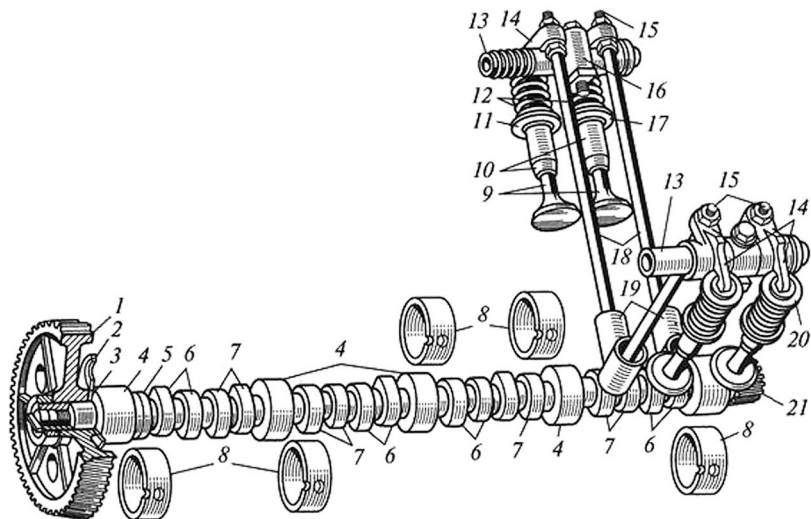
Газораспределительный механизм V-образного двигателя: 1 – зубчатое колесо; 2 – упорный фланец; 3 – распорное кольцо; 4 – передняя опорная шейка; 5 – эксцентрик; 6, 7 – соответственно впускные и выпускные кулачки; 8 – опорные втулки; 9 – клапаны; 10 – направляющие втулки; 11, 17 – шайбы; 12 – пружины; 13 – оси коромысел; 14 – коромысла; 15 – регулировочный винт; 16 – стойки осей коромысел; 18 – штанги; 19 – толкатели; 20 – тарелки; 21 – шестерня привода прерывателя-распределителя и насоса системы смазки
